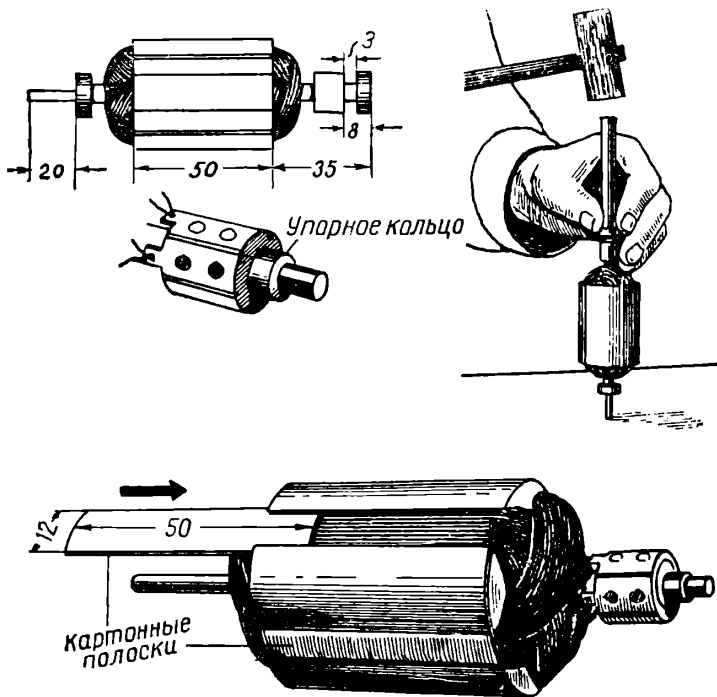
Насадка шариковых подшипников. Собранный ротор двигателя
